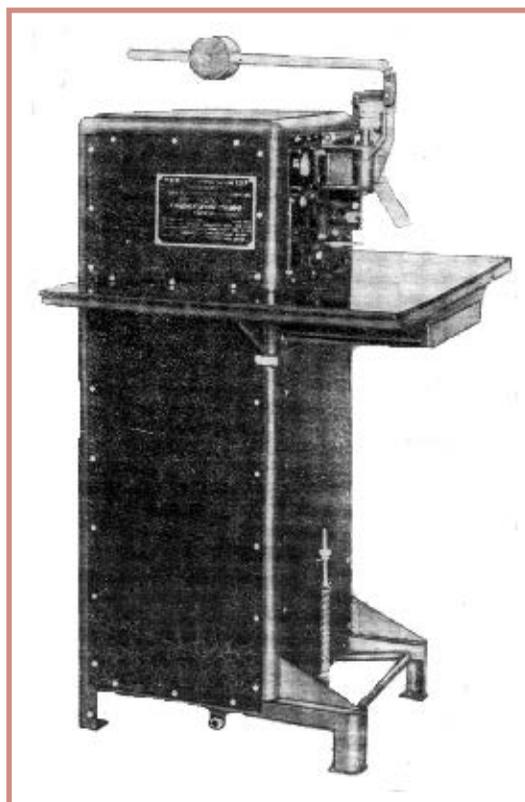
Первая серийная машина для точечной конденсаторной сварки TKM-4
